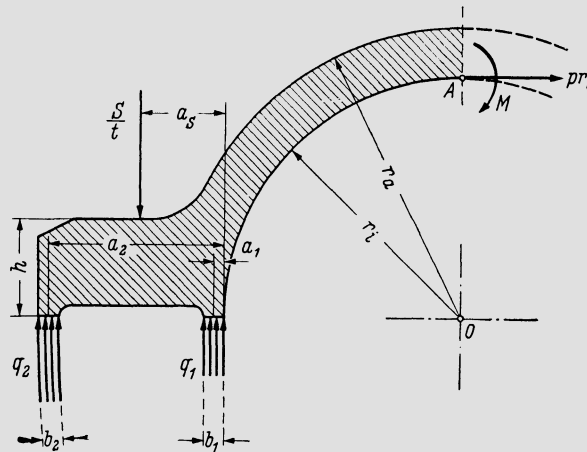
Gleichgewichtsbetrachtung an zylindrischem Gehäuse mit horizontalem Trennflansch
